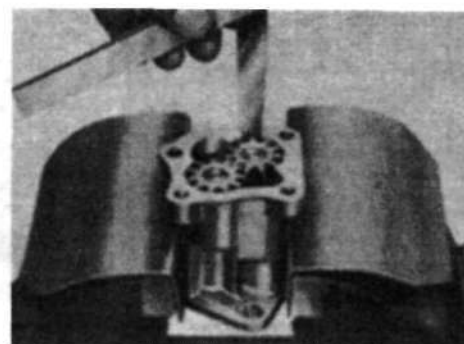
Проверка бокового зазора шестерен масляного насоса (раздел 36): Зазор должен быть равен 0,05-0,14 мм.
